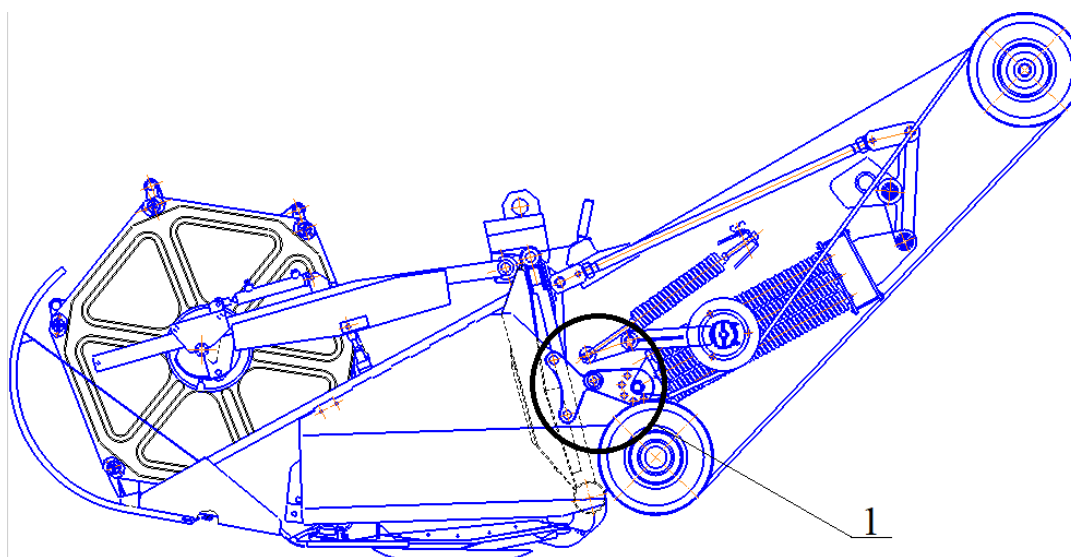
Установка шарнирной опоры в зерноуборочном комбайне: 1 – расположение перенесенной шарнирной опоры
